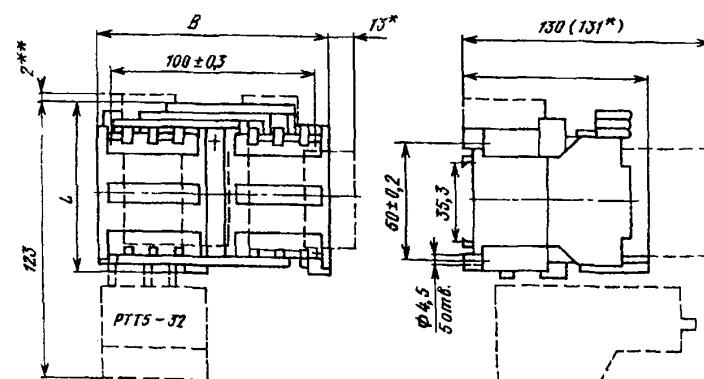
Габаритные и установочные размеры реверсивных пускателей (ПМ12-032)
